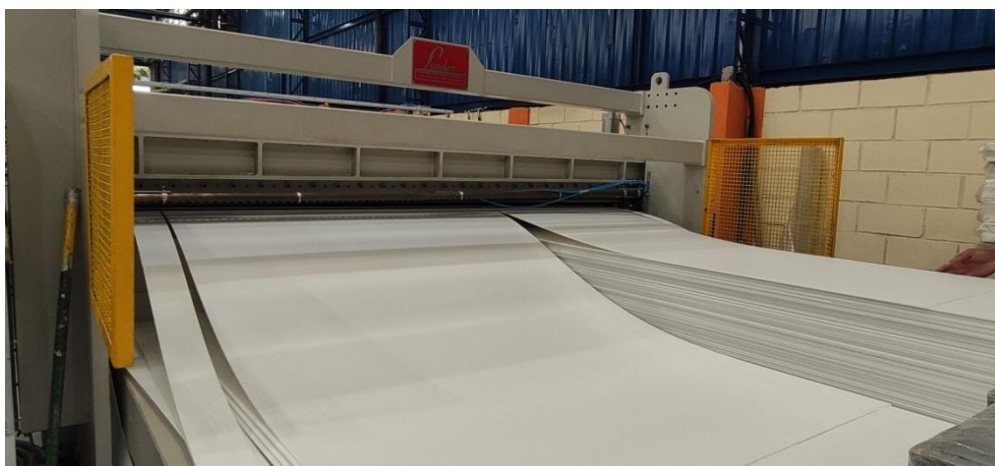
Corte das placas, destacando aparas laterais. Fonte: SMA
